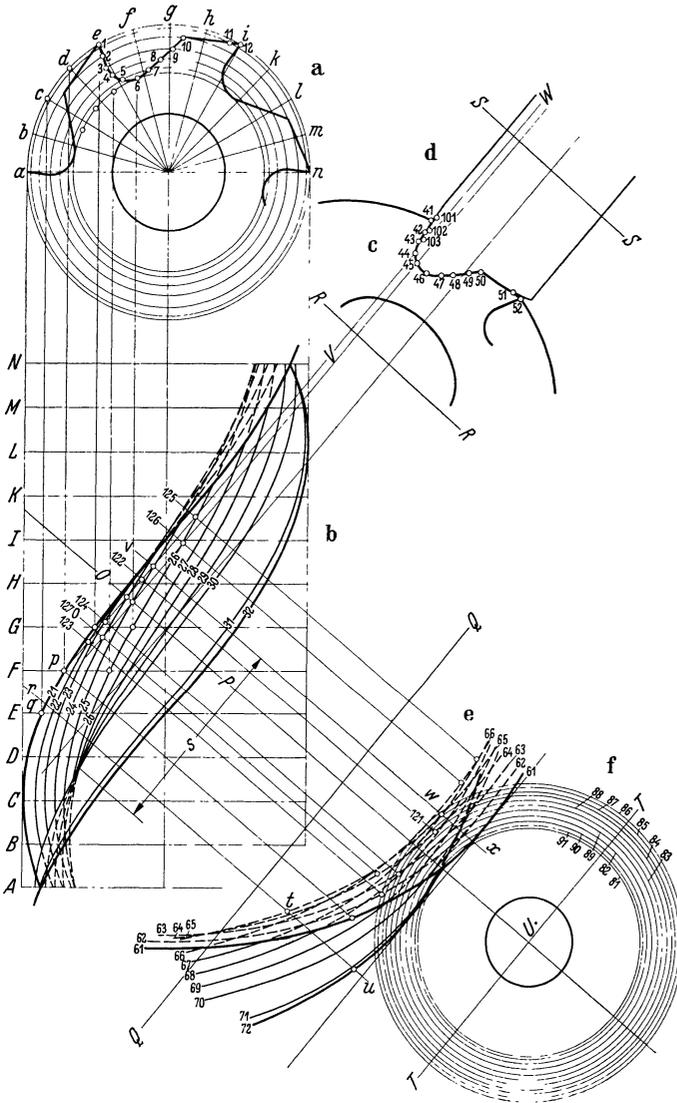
Konstruktion von Profilfräsern zum Spiralfräser¹.
